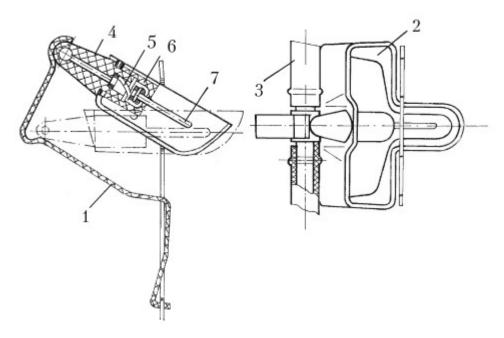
Автопоилка АУ3–80: 1 – подводящий шланг; 2 – чаша; 3 – пружина крепления; 4 – штуцер; 5 – пружина клапана; 6 – корпус клапана; 7 – клапан
